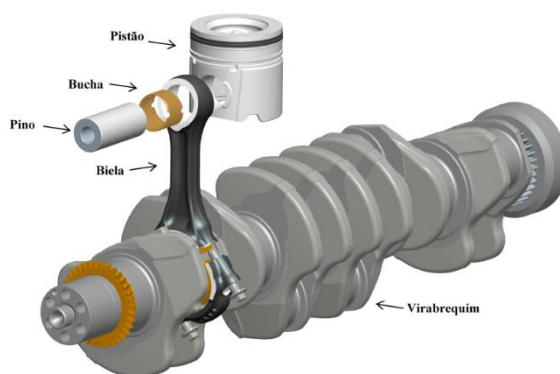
Conjunto pistão-biela-virabrequim do motor.
